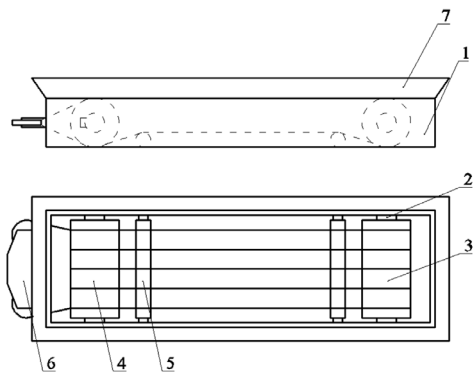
Канатный блок: 1 – рама; 2 – подшипниковый узел; 3 – приводной барабан; 4 – ведомый барабан; 5 – отклоняющие ролики; 6 – натяжное устройство; 7 – борт
